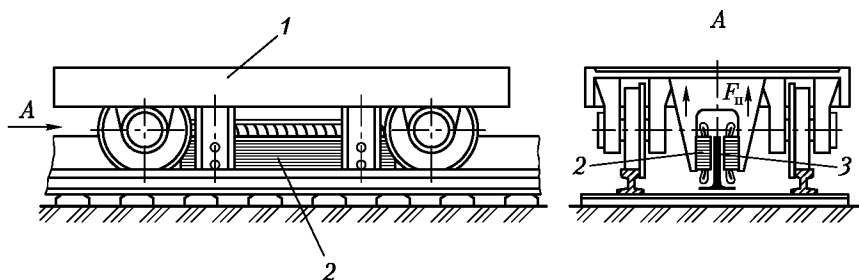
Линейный асинхронный двигатель привода железнодорожного транспортного средства
